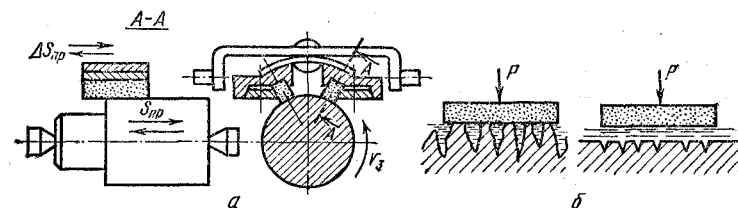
Схема обработки наружной цилиндрической поверхности суперфинишированием
